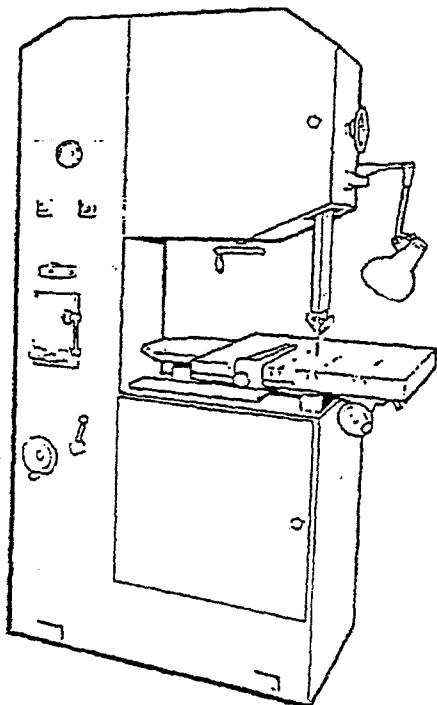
Вертикальний стрічковопиляльний верстат з нерухомою пилальною рамою
